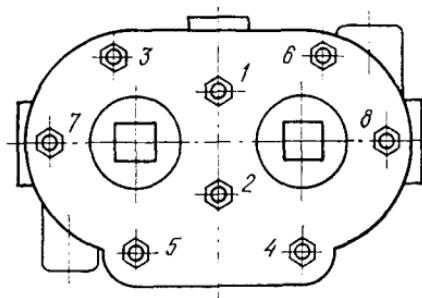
Последовательность затяжки гаек головки блока компрессора
